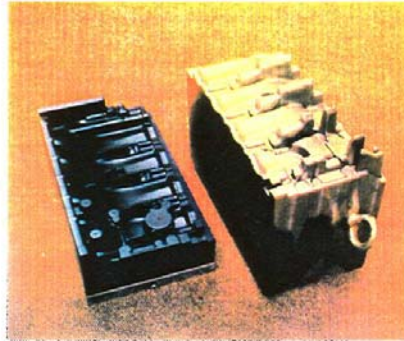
Parte del carter de un motor mecanizado mediante una máquina de electroerosión.
